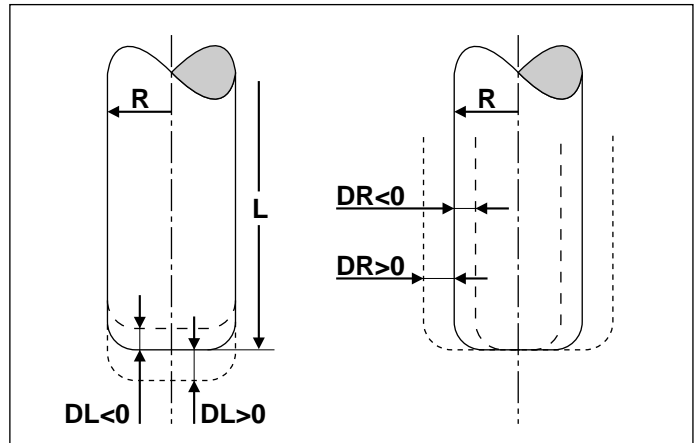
Aufmaße DL, DR beim Eckenradiusfräser
